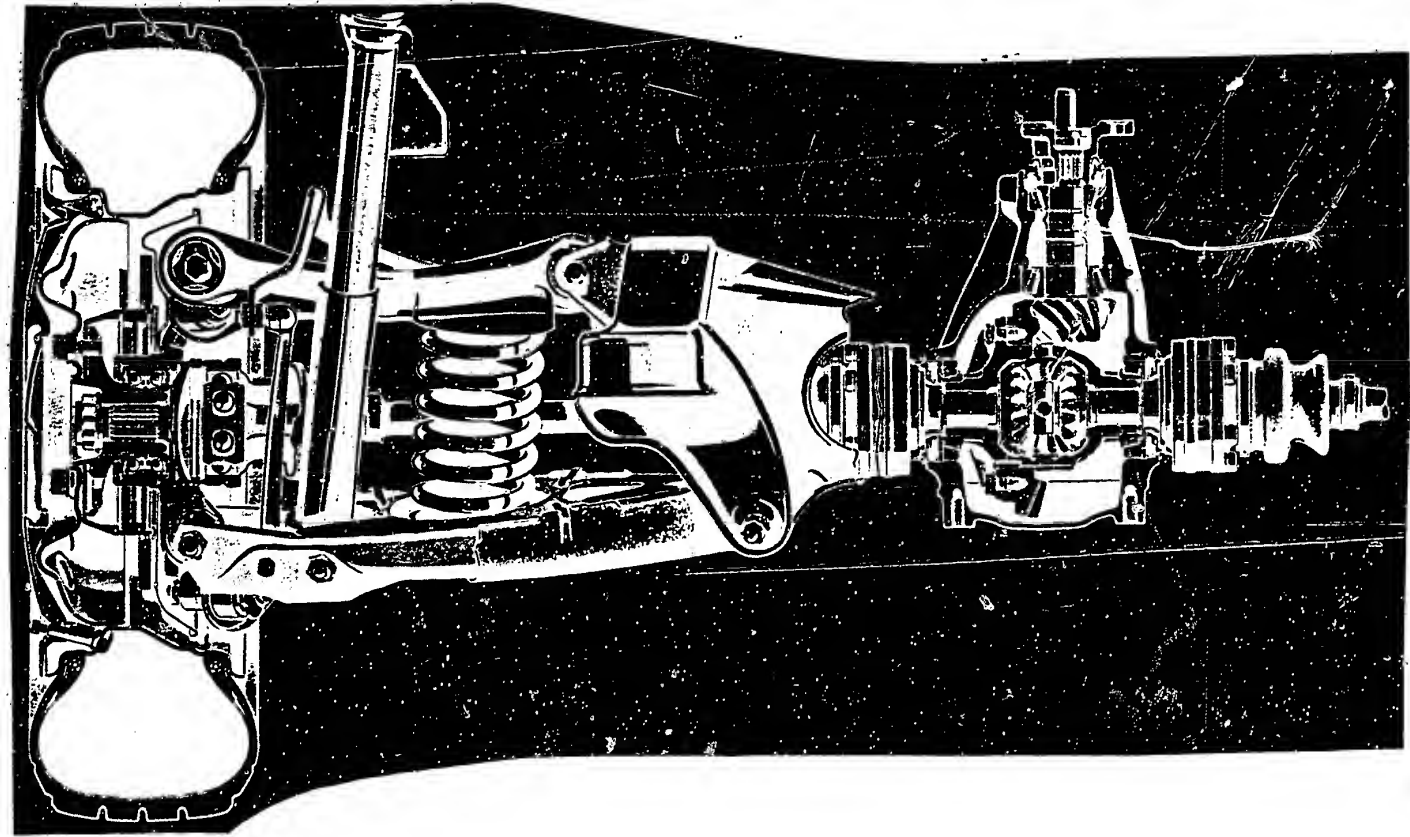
Querschnitt durch die Hinterradaufhängung mit Differential.
